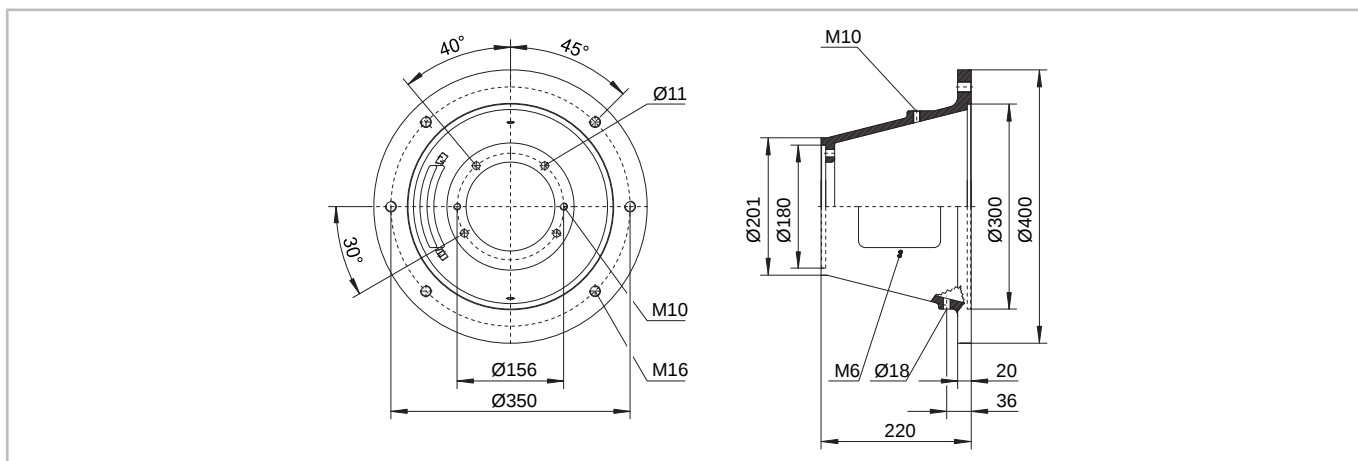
Габаритный чертеж кожуха муфты GS5080
